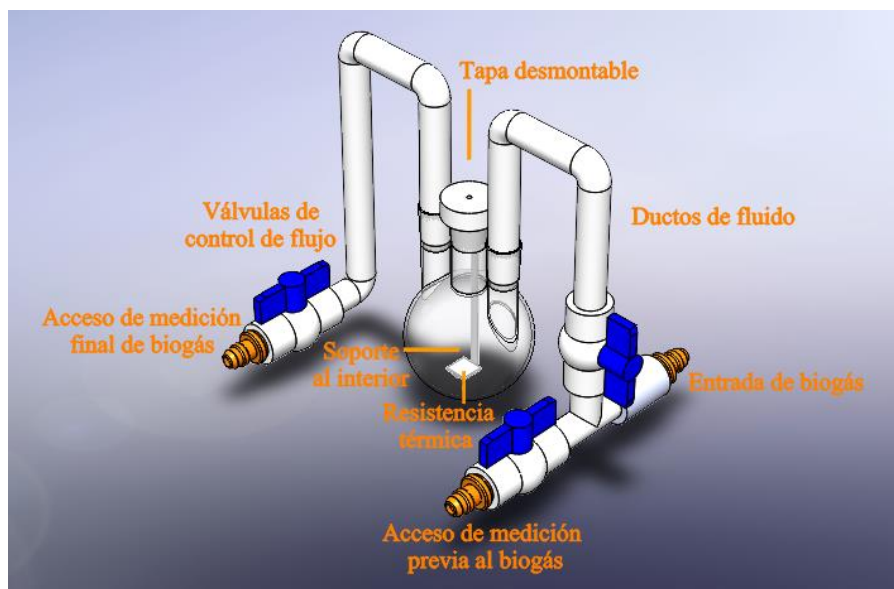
Diseño de la cámara de sensado. Vista isométrica mediante SolidWorks®.
